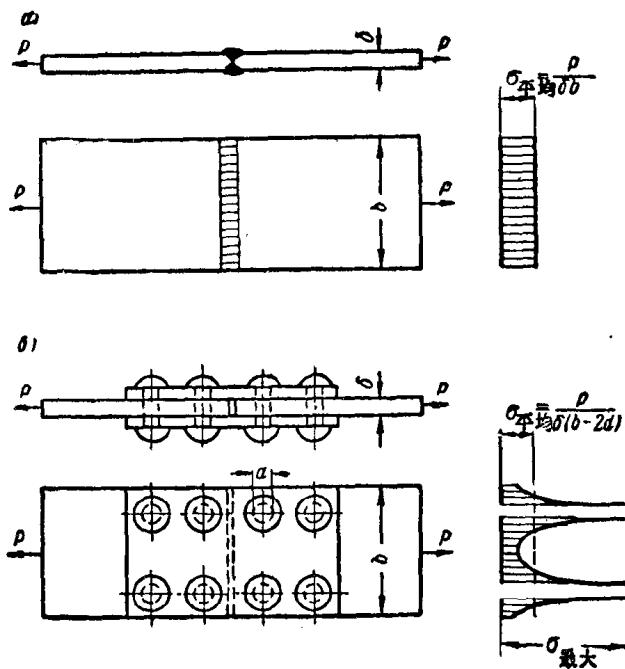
焊接对接接头 (a) 及铆接盖板接头 (b)
